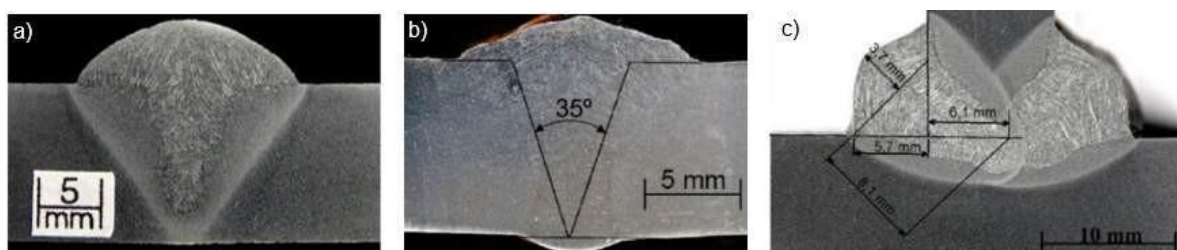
Exemplos de soldas realizadas com o *DynaFlex-Arc*: Em a) Depósito sobre chapa [88]; b) Solda de topo em chanfro V [8]; c) Junta de filete em "T" [9].
